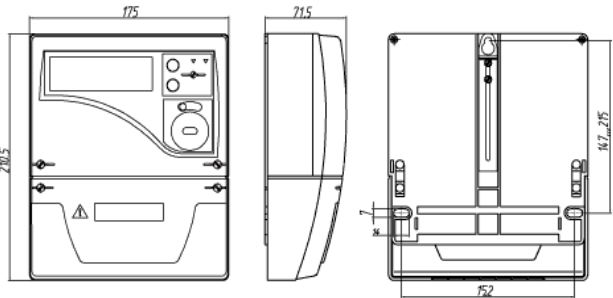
Загальний вигляд лічильника CE303-U в корпусі S31
